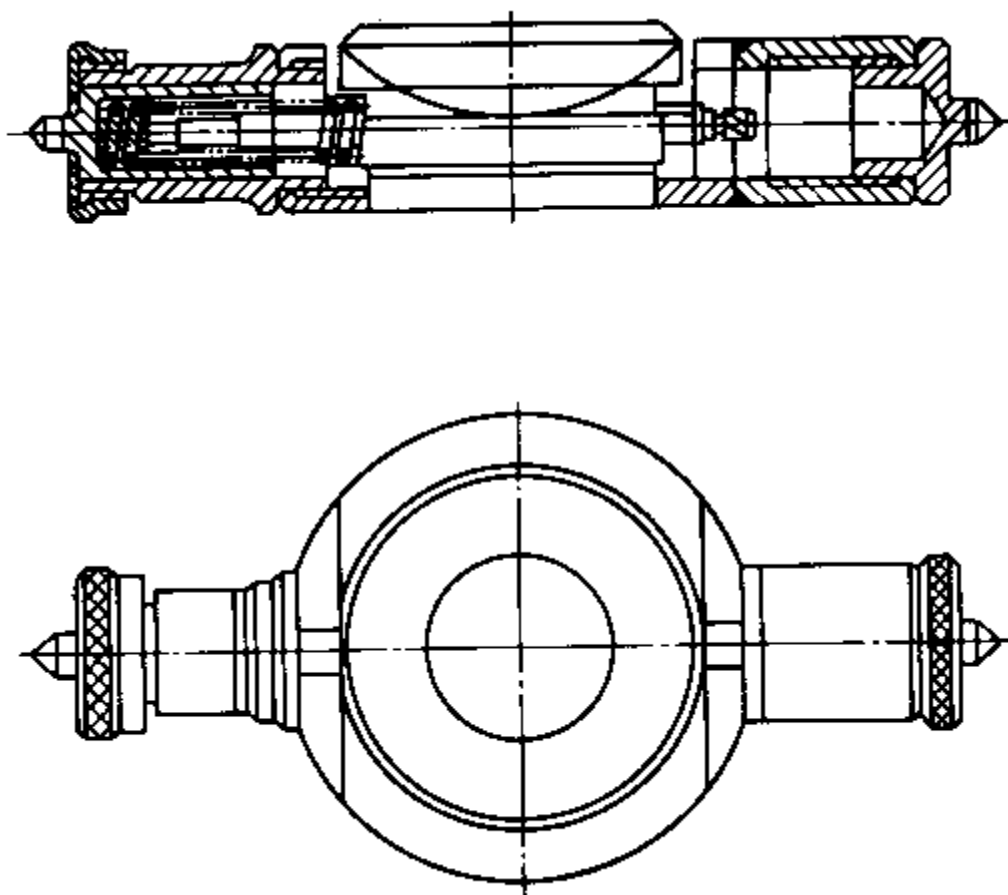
Приспособление для замера раскеса щек коленчатого вала
